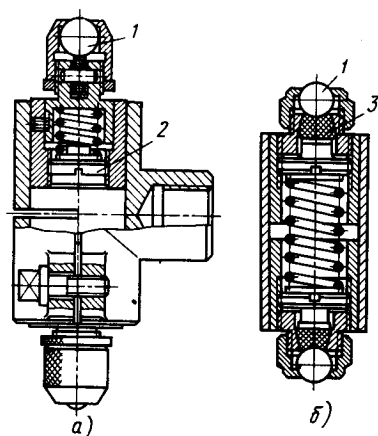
Шариковые раскатки: а – с опорой элементов (шариков) на подшипники; б – с опорой элементов на вставки из фторопласта; 1 – шарик; 2 – регулировочный винт; 3 – вставки из фторопласта
